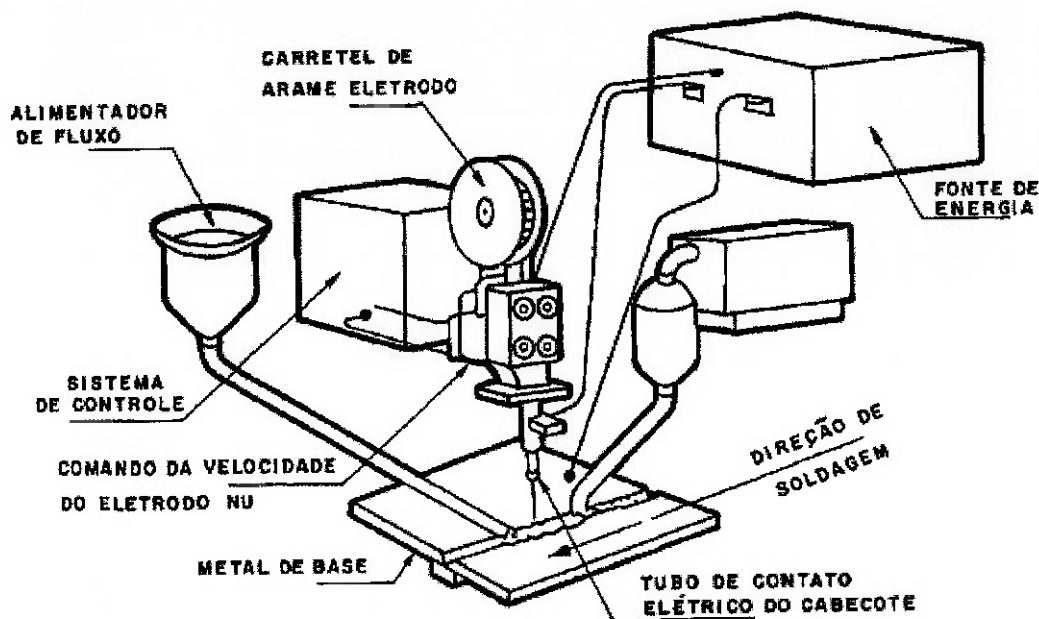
Componentes básicos do equipamento de soldagem com arco submerso automático [5].
